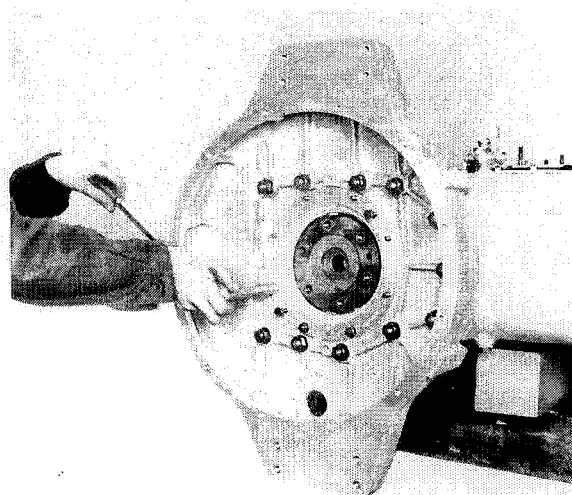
Ausbau der Zylinderbüchsen aus dem Motorgehäuse
